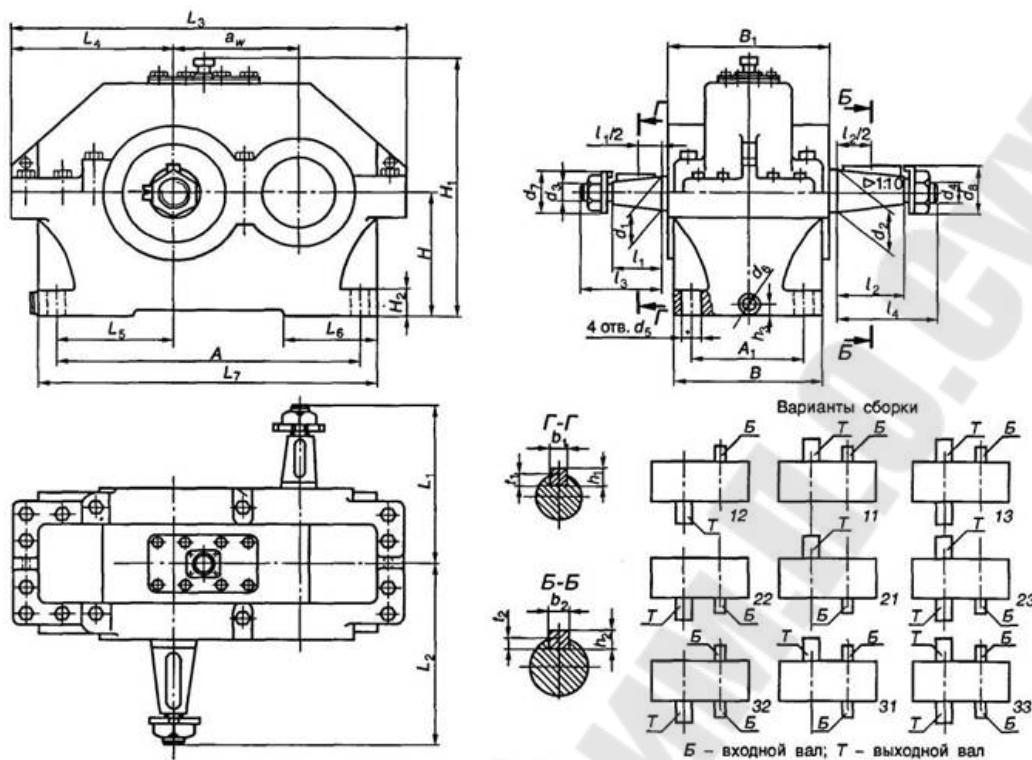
Габаритные и присоединительные размеры цилиндрических одноступенчатых редукторов типа 1ЦУ
